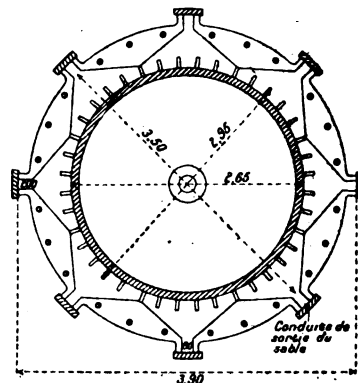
Coupe horizontale d'une pompe-turbine au niveau des conduits de sortie du sable.
